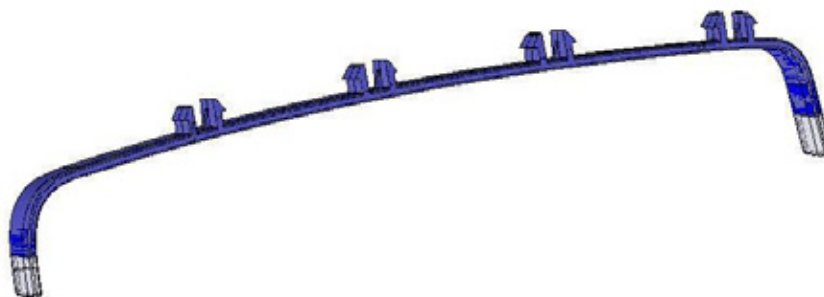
Окончательный вариант детали «Облицовка панели приборов верхняя»
